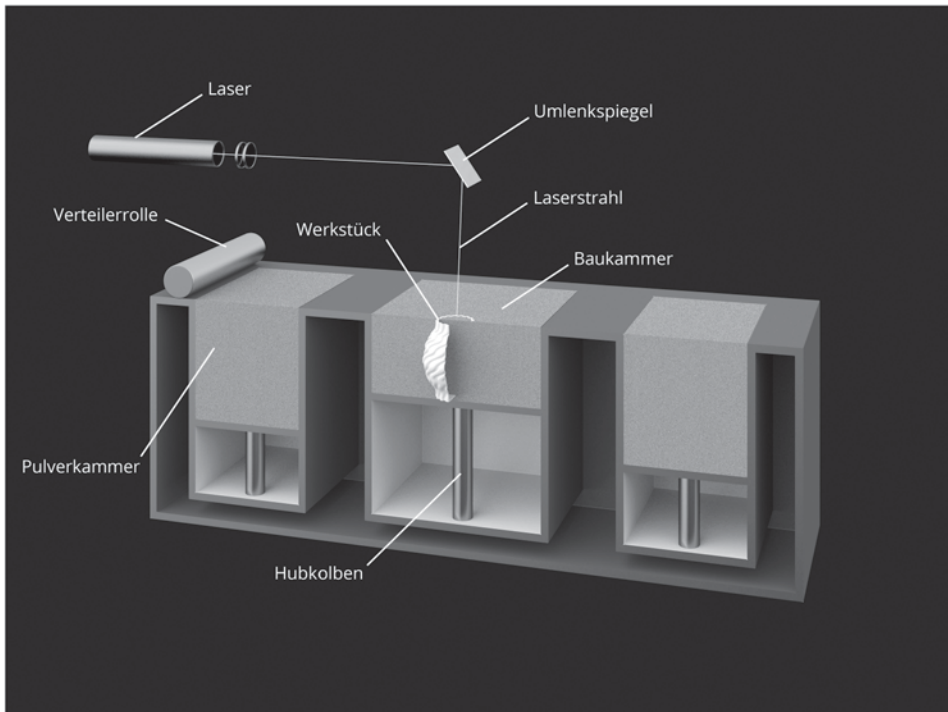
Schemazeichnung Lasersintering-Verfahren (Quelle: Core Consulting GmbH)
